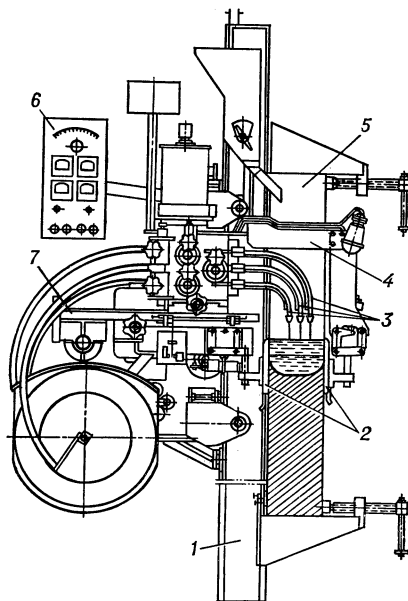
Автомат рельсового типа для электрошлаковой сварки проволочными электродами: 1 — направляющий рельсколонна, закрепляемый на изделии; 2 — передний и задний ползуны; 3 — токоподводящие мундштуки с электродами; 4 — пластина для крепления заднего ползуна; 5 — изделие; 6 — пульт управления; 7 — механизм горизонтальной подачи.
